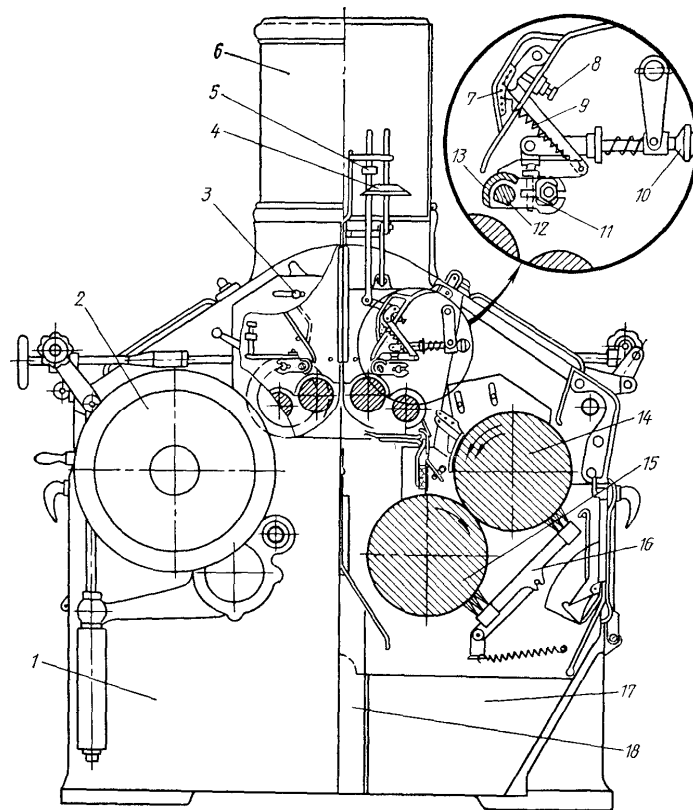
Вальцовий верстат 3М-2: 1 – боковина станини; 2 – ведомий приводний шків; 3 – автомат привалу-відвала; 4 – вимірювальний перетворювач автомата; 5 – вимірювальний перетворювач механізму автоматичного регулювання живлення (продуктивності); 6 – прийомна труба (циліндр); 7 – планка пружини; 8 – болт-обмежник; 9 – пружина вимірювального перетворювача; 10 – гвинт-ручного регулювання; 11 – ексцентрикова втулка; 12 – коромисло; 13 – живильна заслінка; 14 – швидко-обертаючий валець; 15 – повільнообертаючий валець; 16 – щітки для очищення вальців; 17 – бункер; 18 – аспіраційна коробка.
